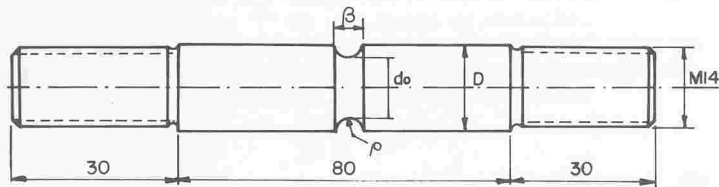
Dimensões principais do corpo de prova cilíndrico com entalhe circunferencial.
